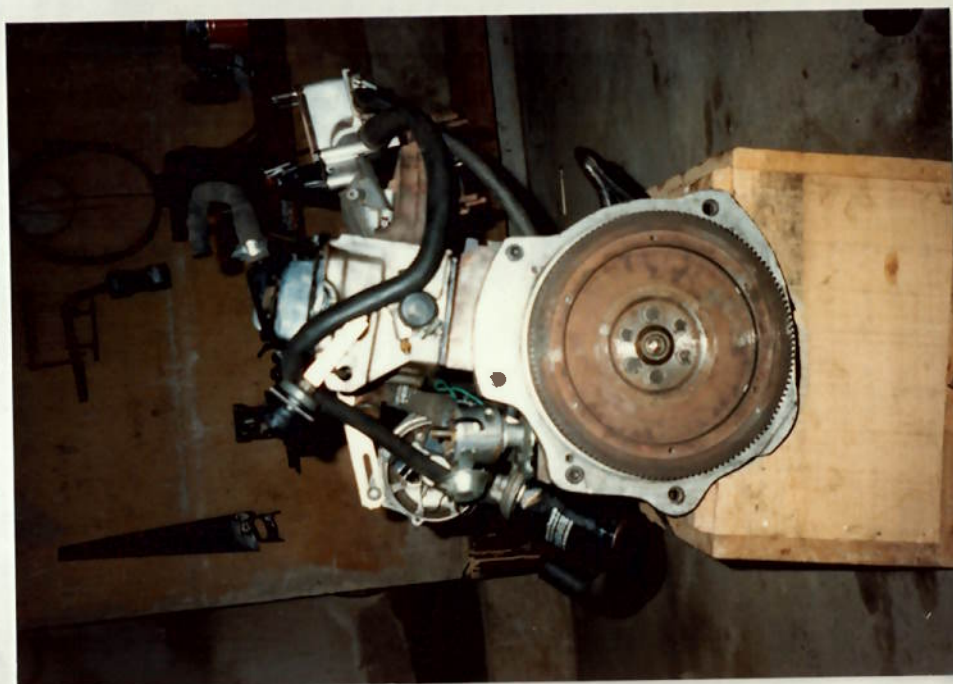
Vista frontal do motor mostrando o flange de adaptação à caixa de câmbio e o volante do motor.
